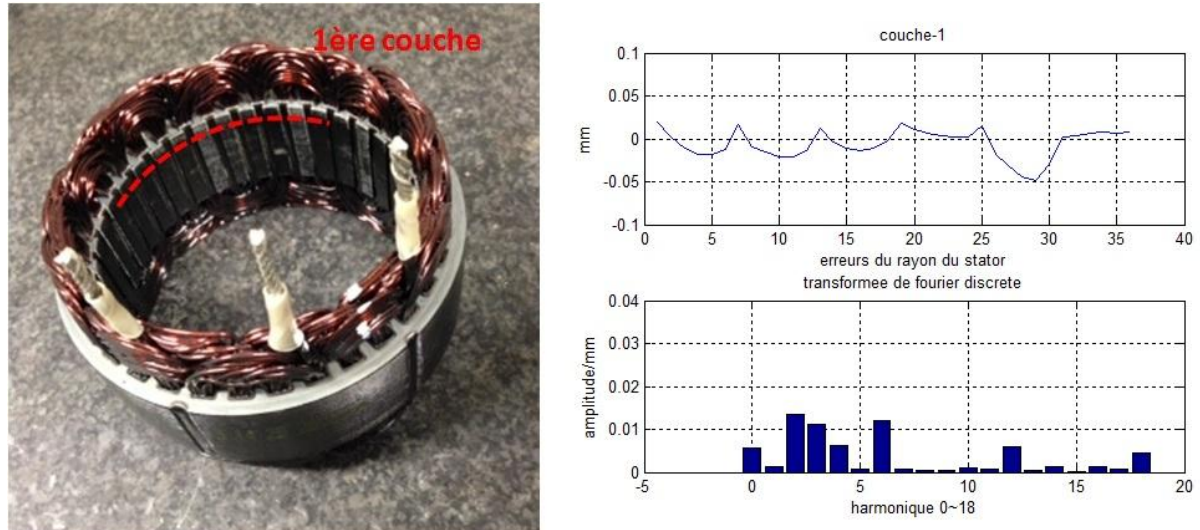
La première couche du stator bobiné (Lot stator bobiné, Numéro 3)
